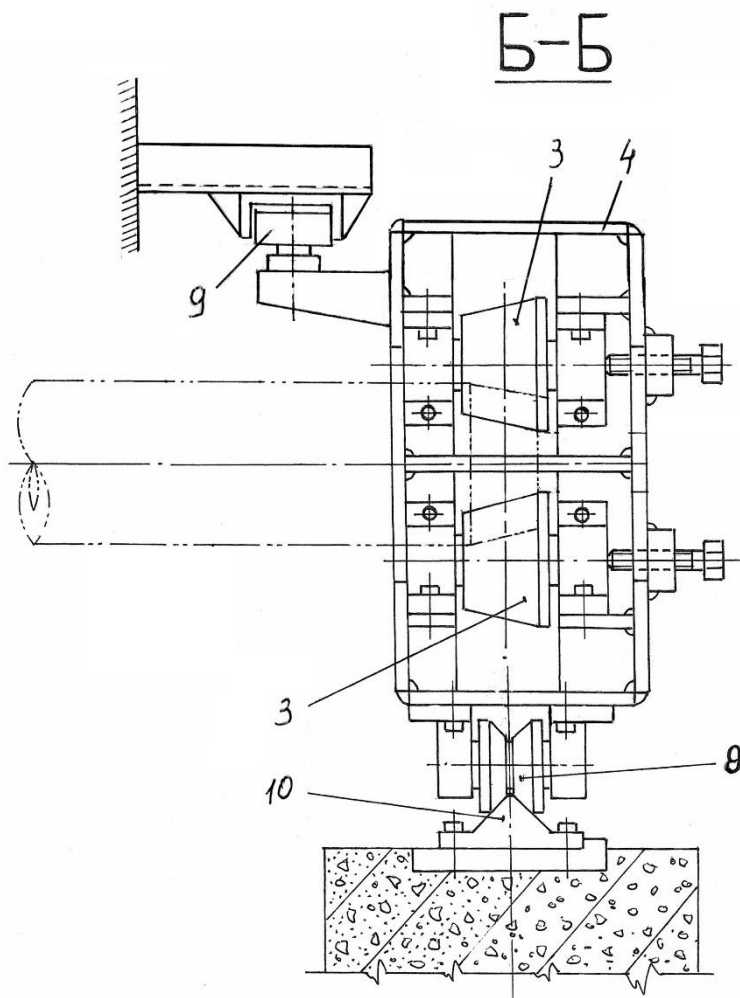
Обкатний пристрій (розріз Б-Б на рис. 4)
